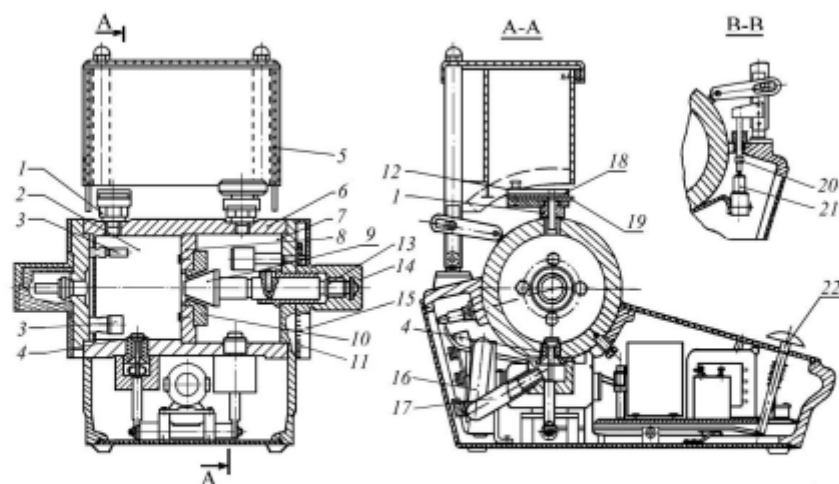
Устройство стенда ОТ 17 для определения величины тушащего зазора:
